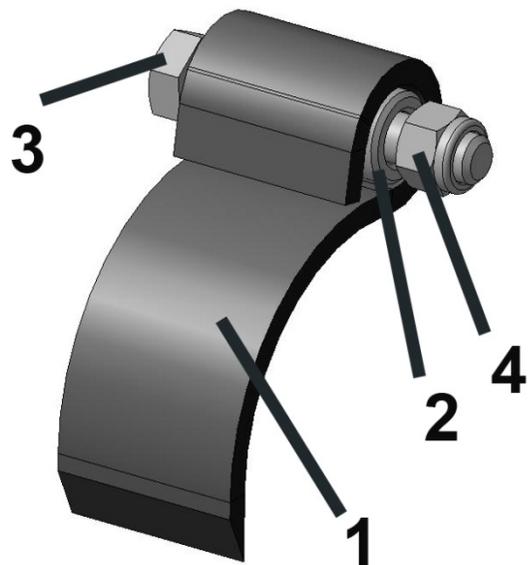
ИРО 03.500 Нож в сборе (короткий)
